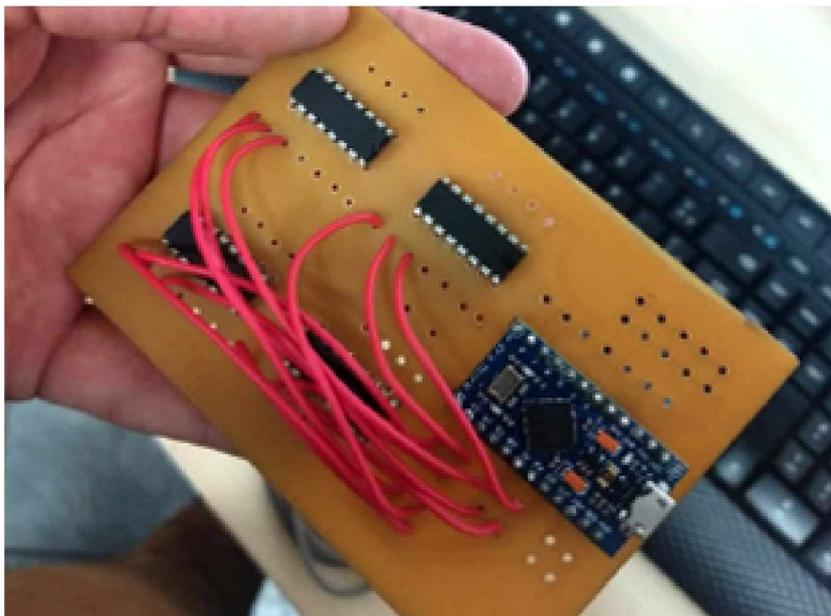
Primeira etapa da soldagem da PCI. Fonte: autoria própria
